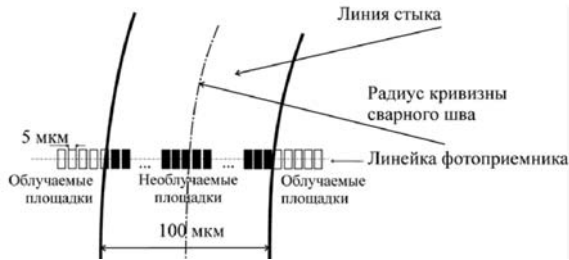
Положение много площадочной линейки фотоприемников относительно сварного шва на криволинейной поверхности свариваемых элементов детали
